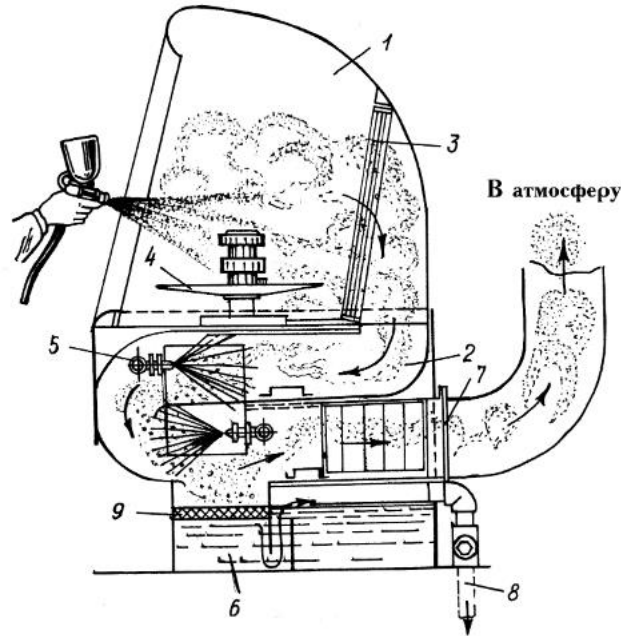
Камера з гідрофільтрами для нанесення лаку пневматичним розпилюванням: 1 - корпус; 2 - коробка гідрофільтра; 3 - лаковловлювальна решітка; 4 - поворотний стіл; 5 - водорозпилювальні форсунки; 6-водяна пастка; 7 - водовідокремлювач; 8- зливна труба ; 9 - відстій лаку (фарби) .
